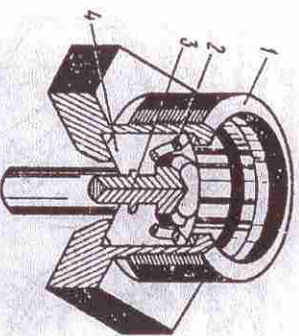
Вентиль спускной: 1 — корпус; 2 — пружина; 3 — шток; 4 — прокладка
